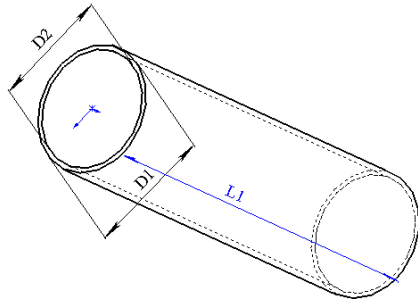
Етап 1 щодо креслення циліндра
